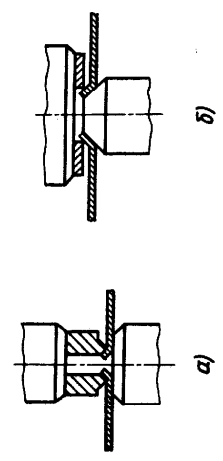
Схемы приварки бобышки (а) и фланца (б)
